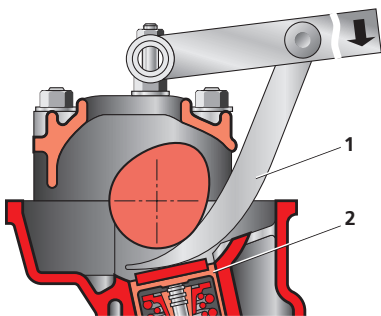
Утапливание толкателя клапана при замене регулировочной шайбы: 1 — приспособление; 2 — толкатель
